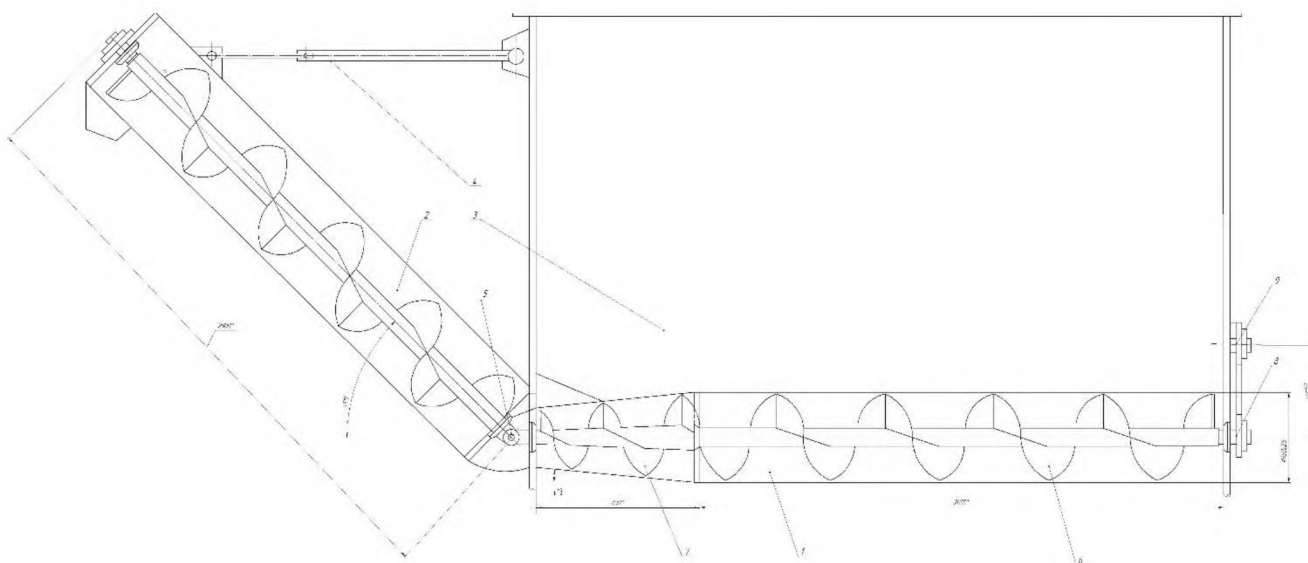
Пристрій вивантаження сапропелю: 1- горизонтальний шнек; 2- похилий шнек; 3- накопичувальна ємкість; 4- тяга; 5- шарнірне з'єднання; 6- циліндрична частина; 7- конічна частина; 8- привід шнеків; 9- ланцюгова передача
